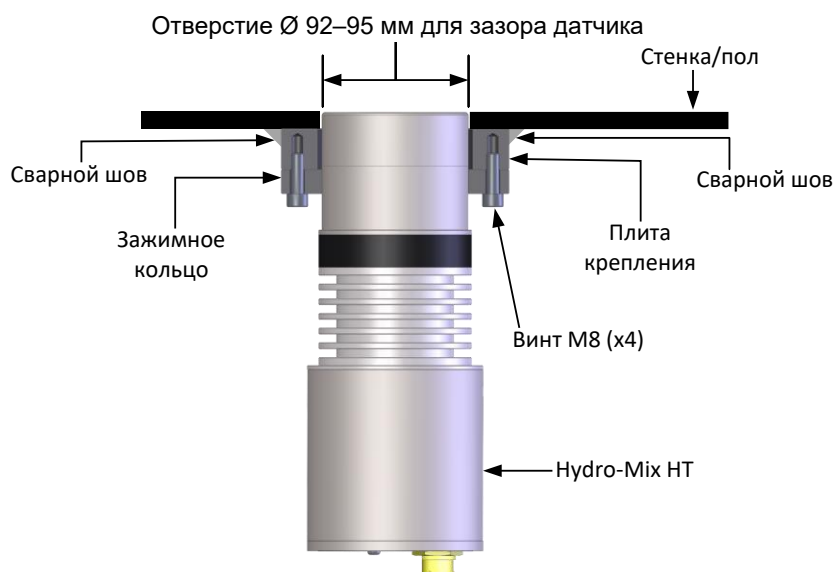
Установка датчика (наружный монтаж плиты крепления)
